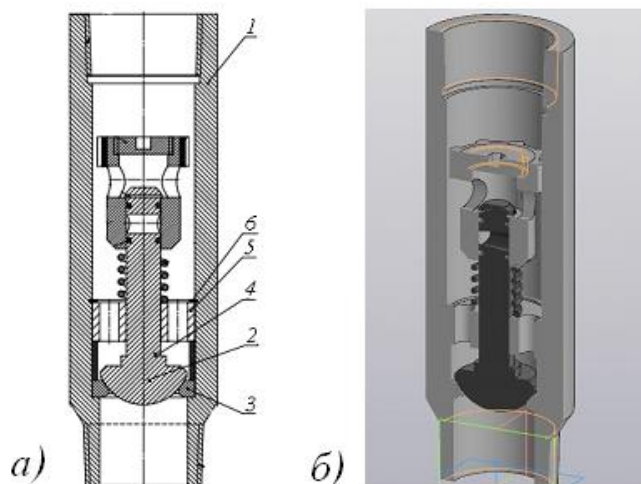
Обратный клапанный узел с каплевидной формой тарелки:
